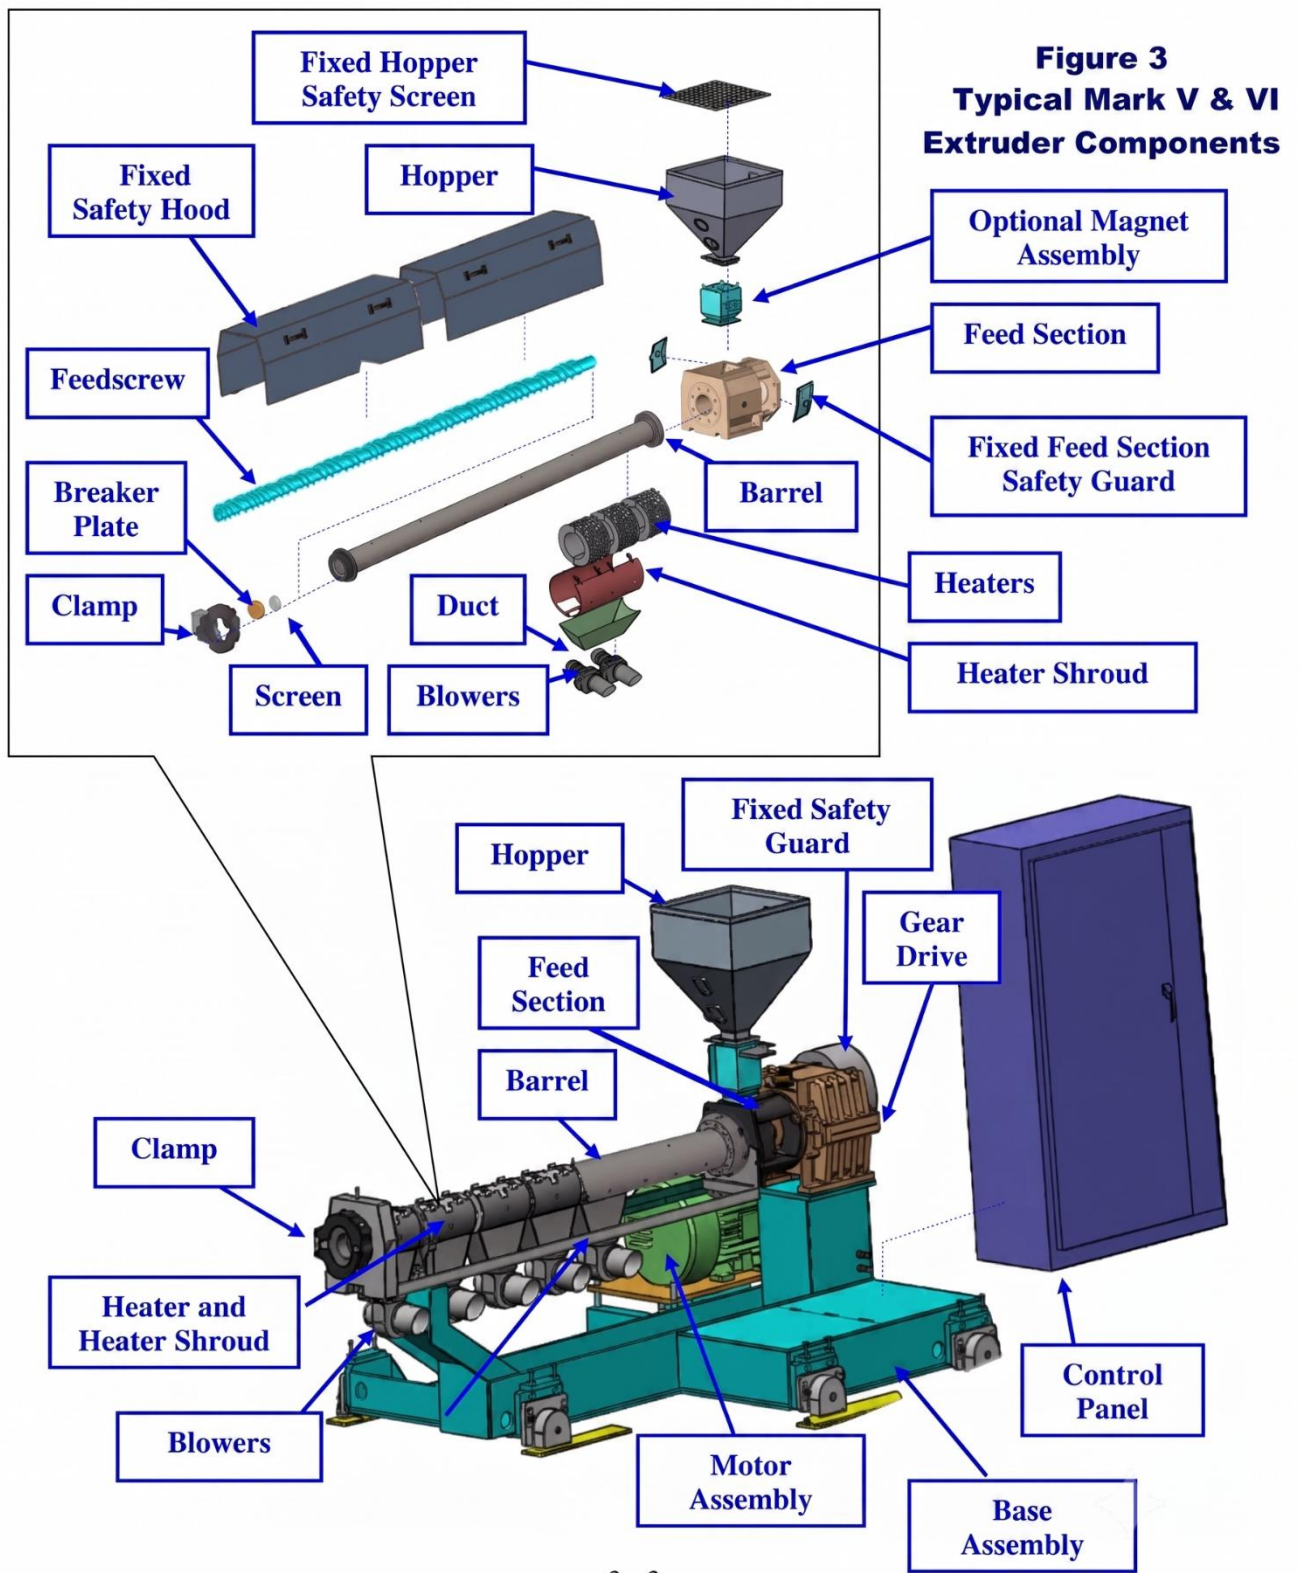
Componentes Típicos da Extrusora Mark V & VI: Detalha a Tela de Segurança Fixa do Funil, Placa Rompedora (Breaker Plate), Duto, Tela, Aquecedores, Carenagem do Aquecedor, e Conjunto Magnético Opcional.
